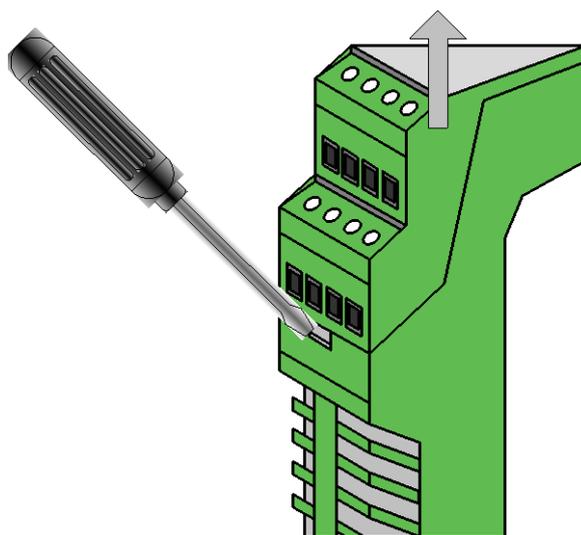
Извлечение платы блока ВСП-14-1 из корпуса
